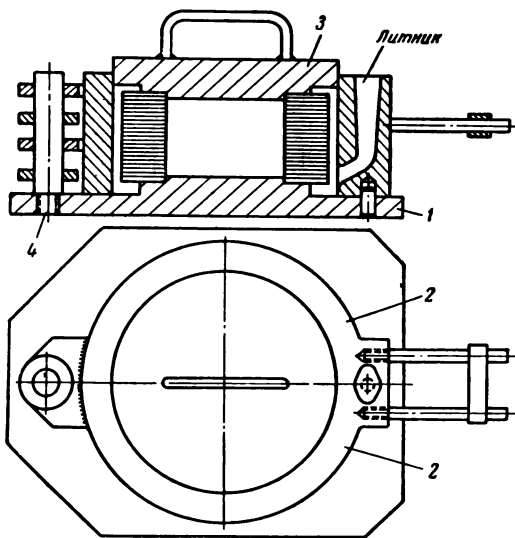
Форма для заливки статора в алюминиевую оболочку.
